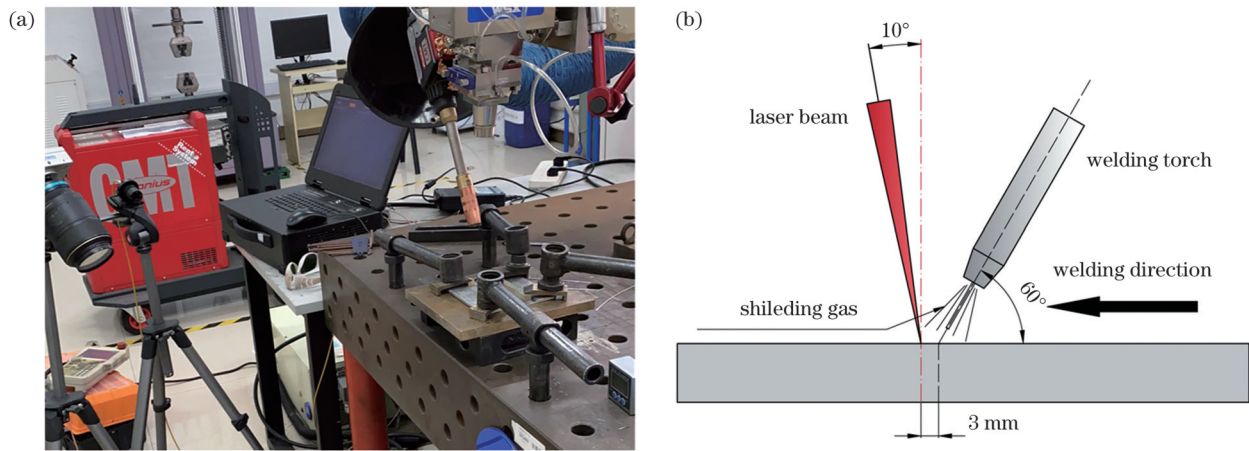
激光-CMT 焊接图。(a) 试验现场图; (b) 焊接示意图
